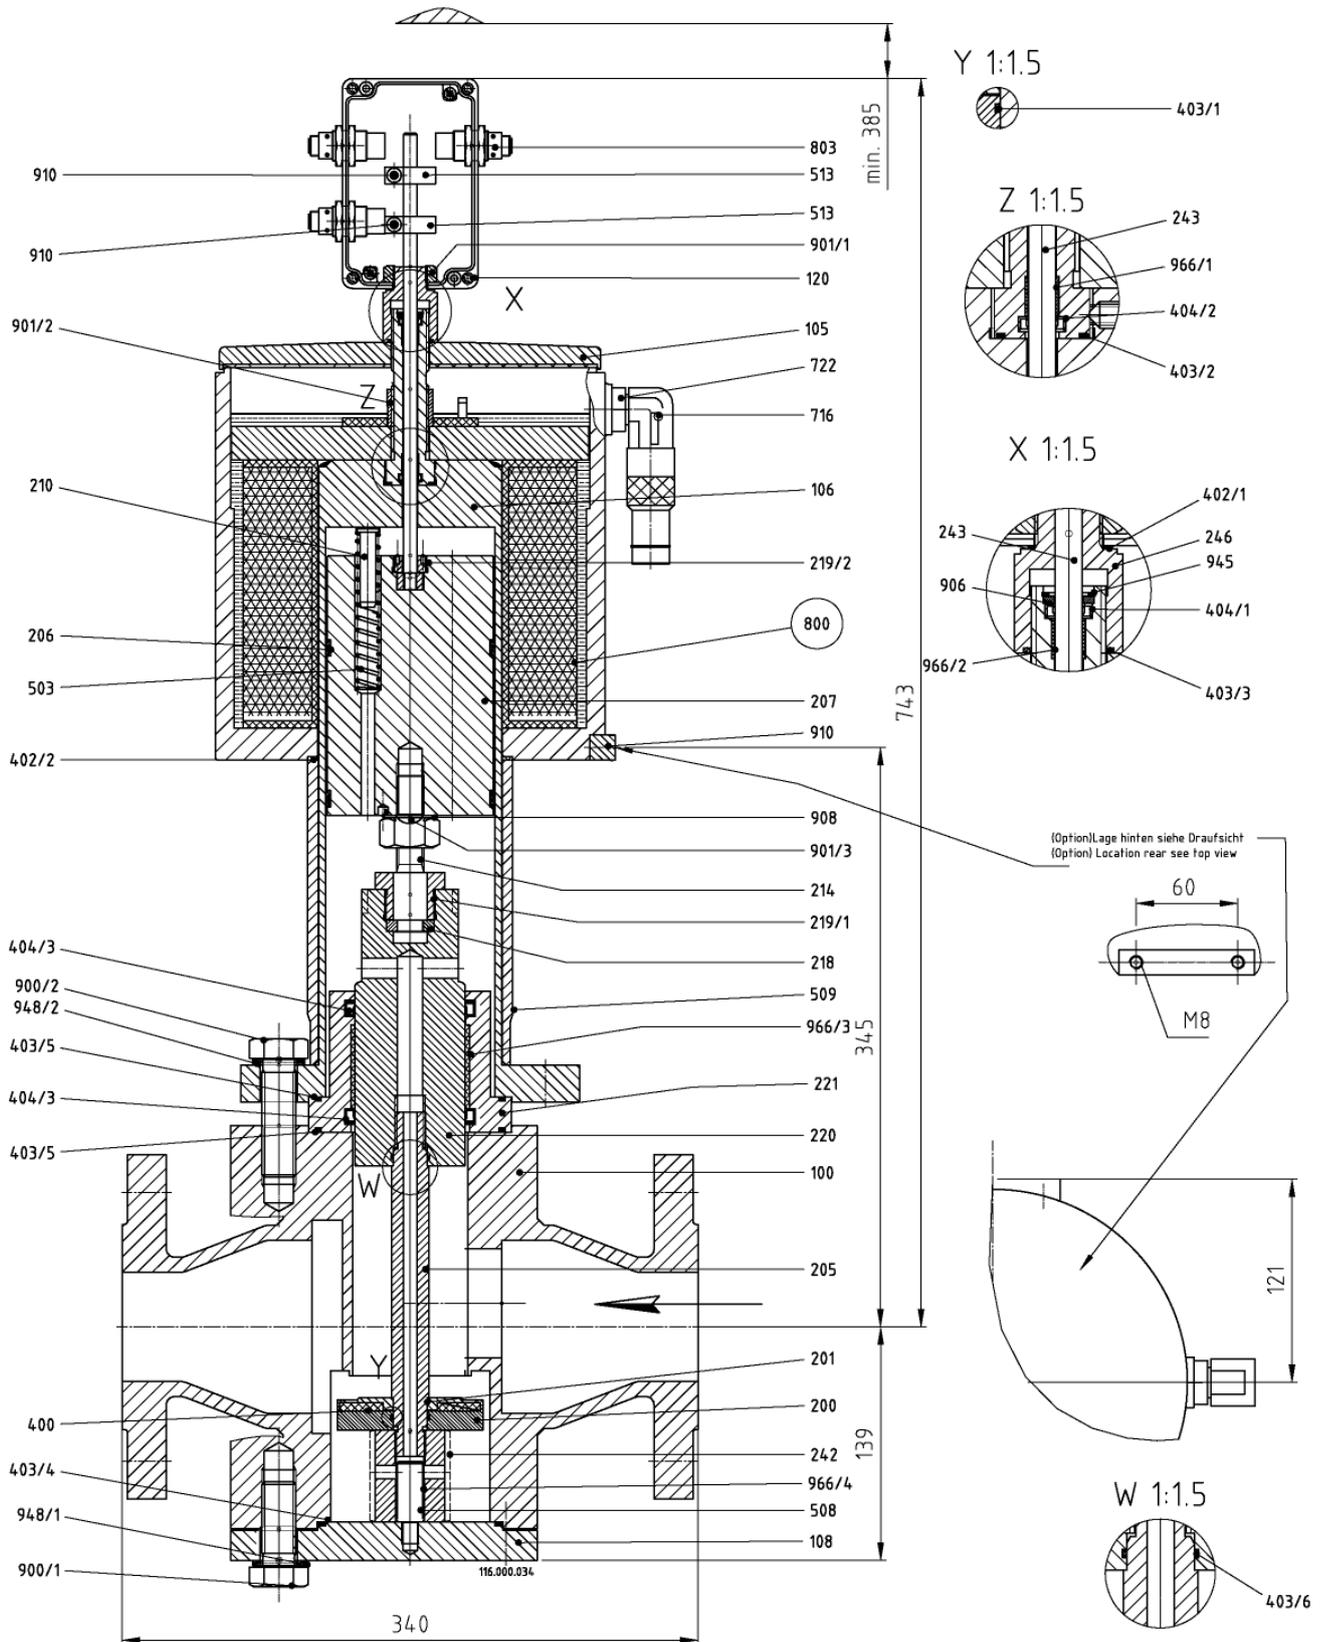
Flanschausführung 55- EVSO 15NH-4R...
